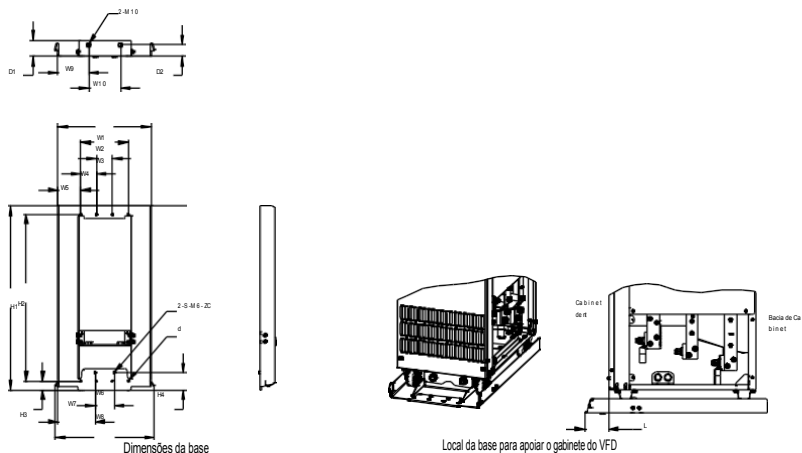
Dimensões do suporte da base do VFD 380V 220-500kW e dimensões de montagem Tabela C-8 Dimensões do suporte da base do VFD 380V 220-500kW (unidade: mm)
